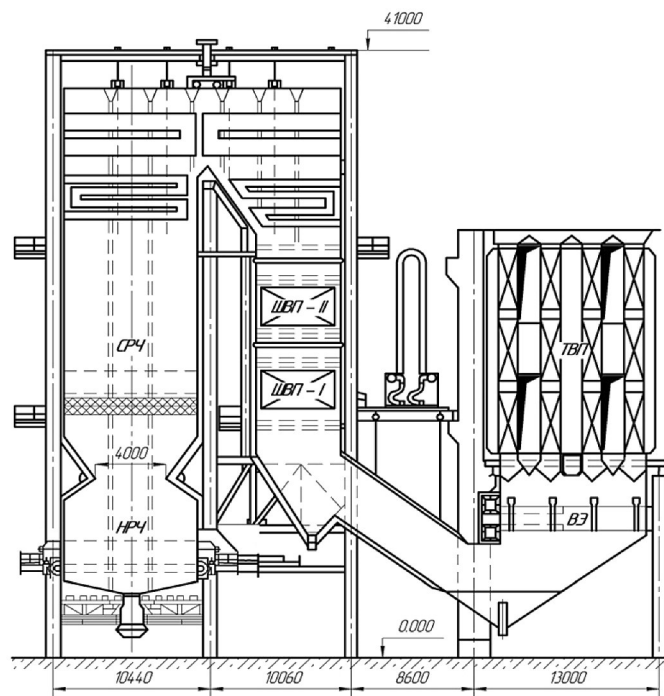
Общий вид корпуса котла П-49 ст. № 7 Назаровской ГРЭС
